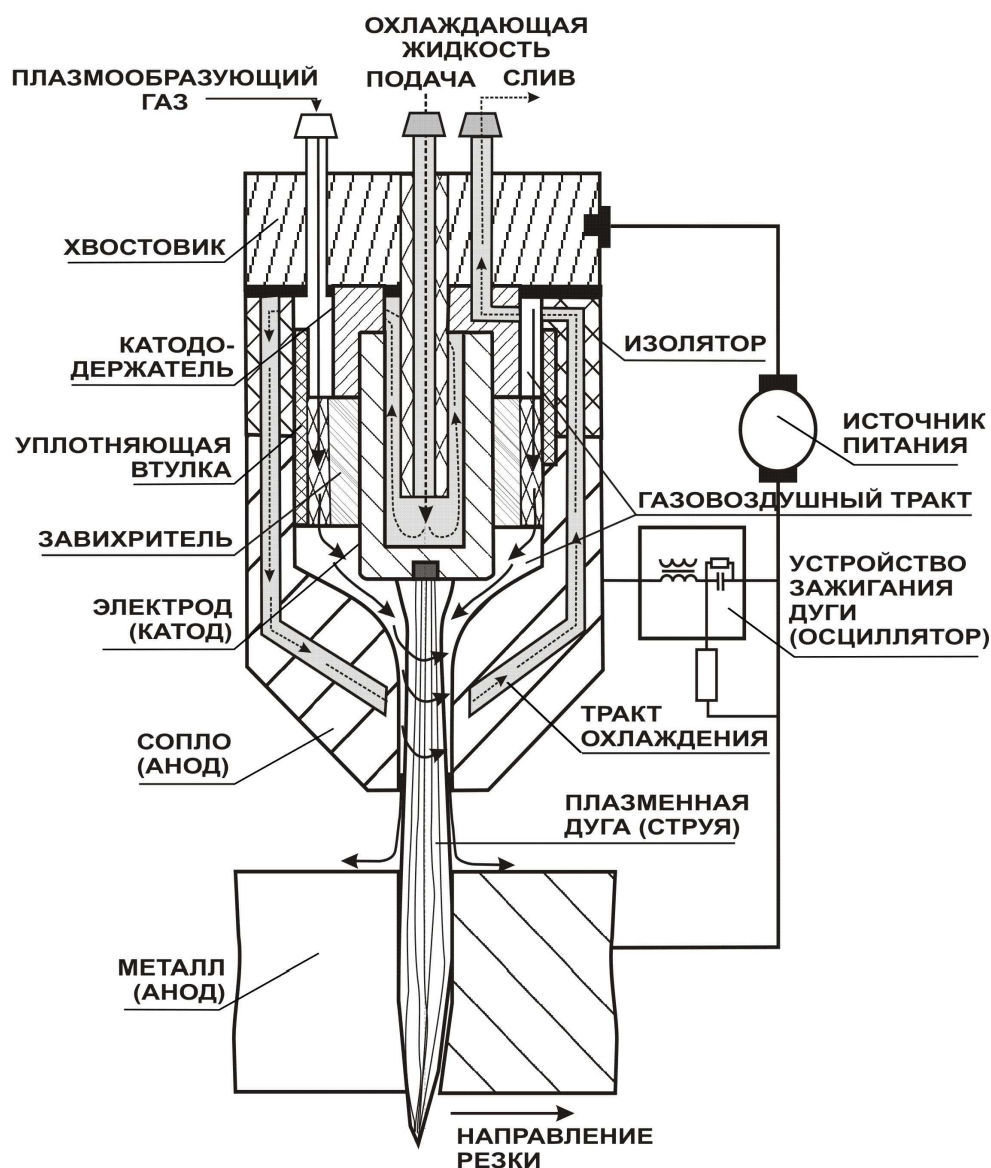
Конструктивная схема плазмотрона для резки металла (прямая полярность)
